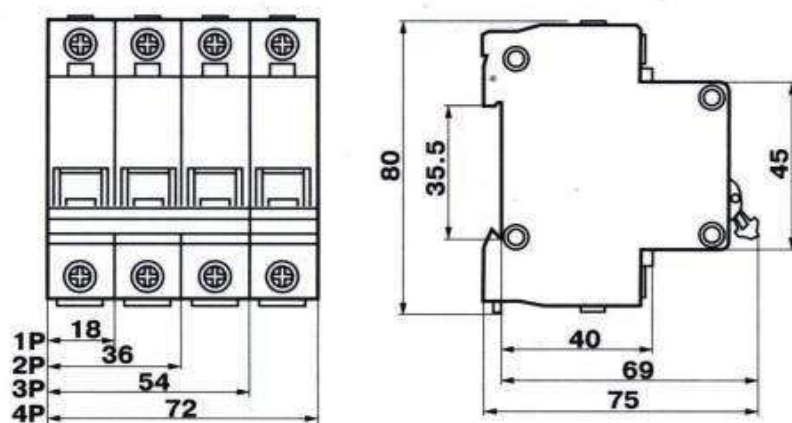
Габаритные и установочные размеры ВН-32 (4 полюса)
